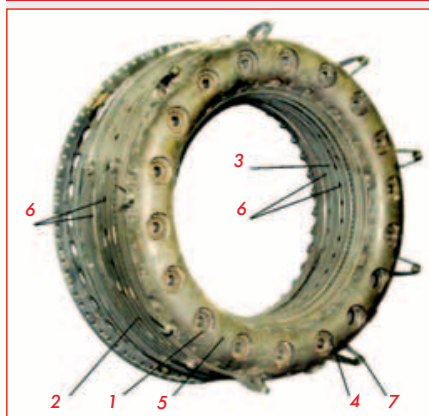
Жаровая труба кольцевой камеры сгорания: 1, 4 - места расположения форсунок; 2, 3 - наружный и внутренний смесители; 5 - фронтное устройство; 6 - отверстия для подвода вторичного воздуха
